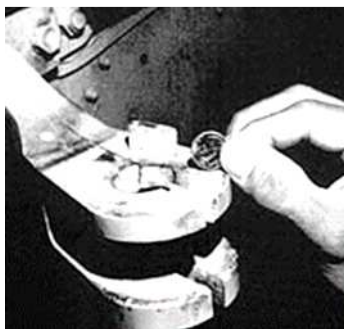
Корозійне розтріскування поковки сплава 7079-T6
